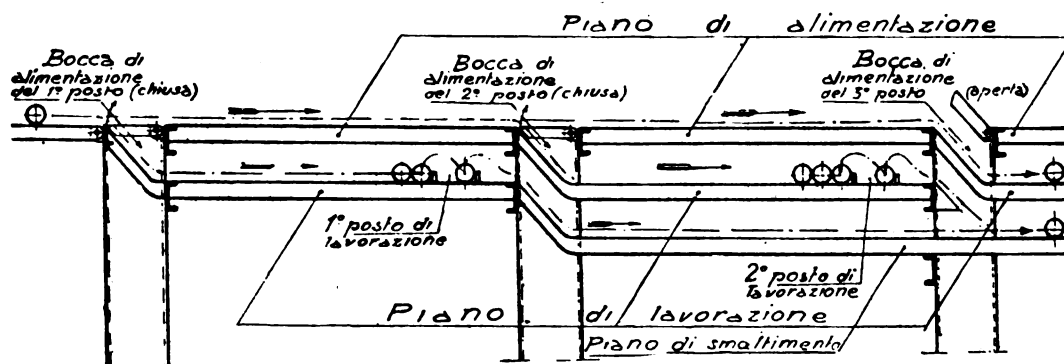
Particolare schematico dei posti di lavorazione in parallelo.
